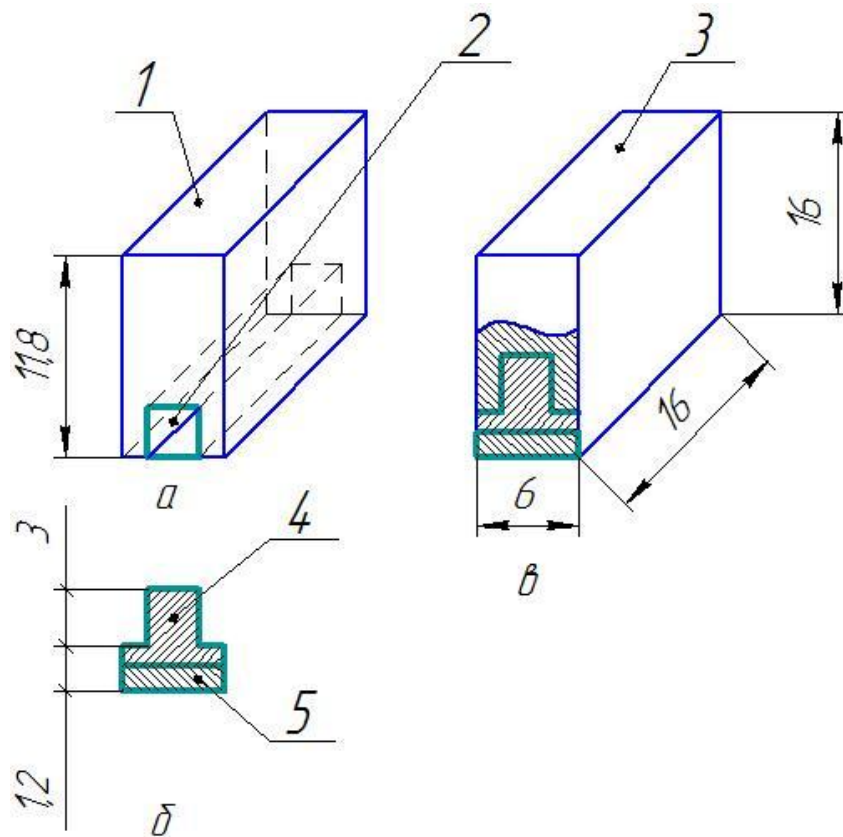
Зразки для випробувань зносостійкості: а) - прямокутна заготовка; б) Т подібна вставка з основним і наплавленим металом; в) – готовий зразок для випробувань на машині НК-М: 1 – заготовка; 2 – проріз; 3 – готовий зразок; 4 – основний метал ; 5 - наплавлений метал
